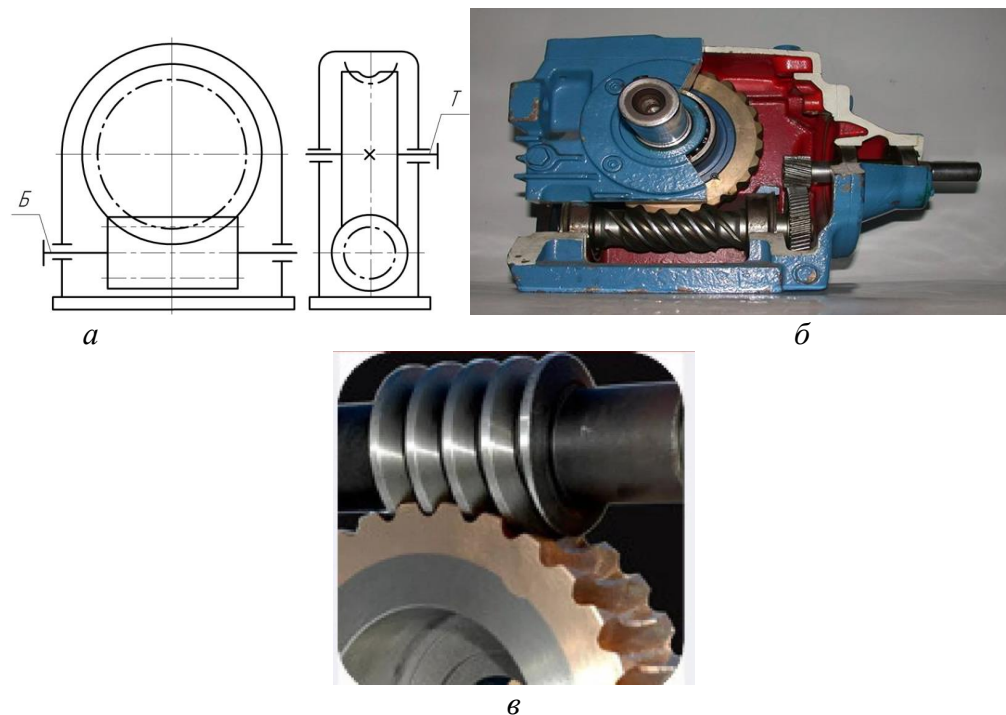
Червячная передача: *а* – кинематическая схема; *б* – внешний вид редуктора с нижним расположением червяка; *в* – зацепление передачи.
